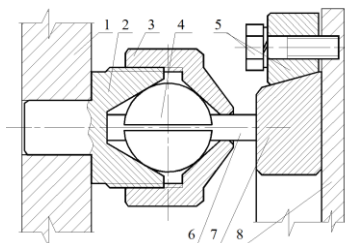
Конструкція сферично-цилінгового затискача: 1 – нерухомий супорт машини; 2 – сідло; 3 – цилінгова гайка; 4 – сферичний шарнір; 5 – фіксатор контргтіла; 6 – зразок; 7 – контргтіло; 8 – рухома планшайба машини тертя
